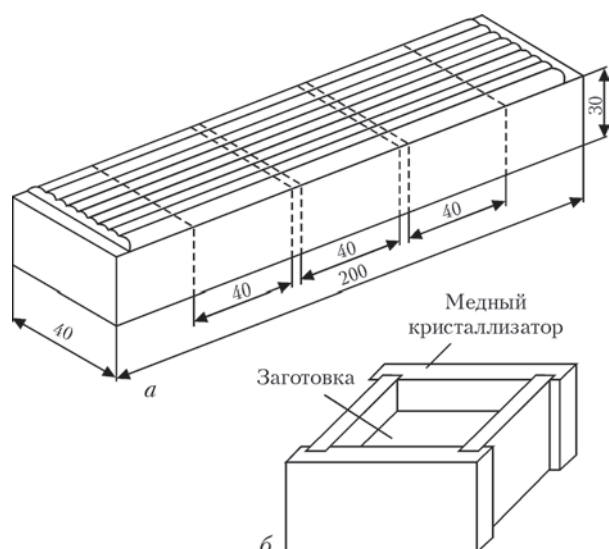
Схема изготовления многослойных наплавленных образцов для исследования термической стойкости: а — при автоматической наплавке под флюсом; б — при полуавтоматической наплавке самозащитными порошковыми проволоками
